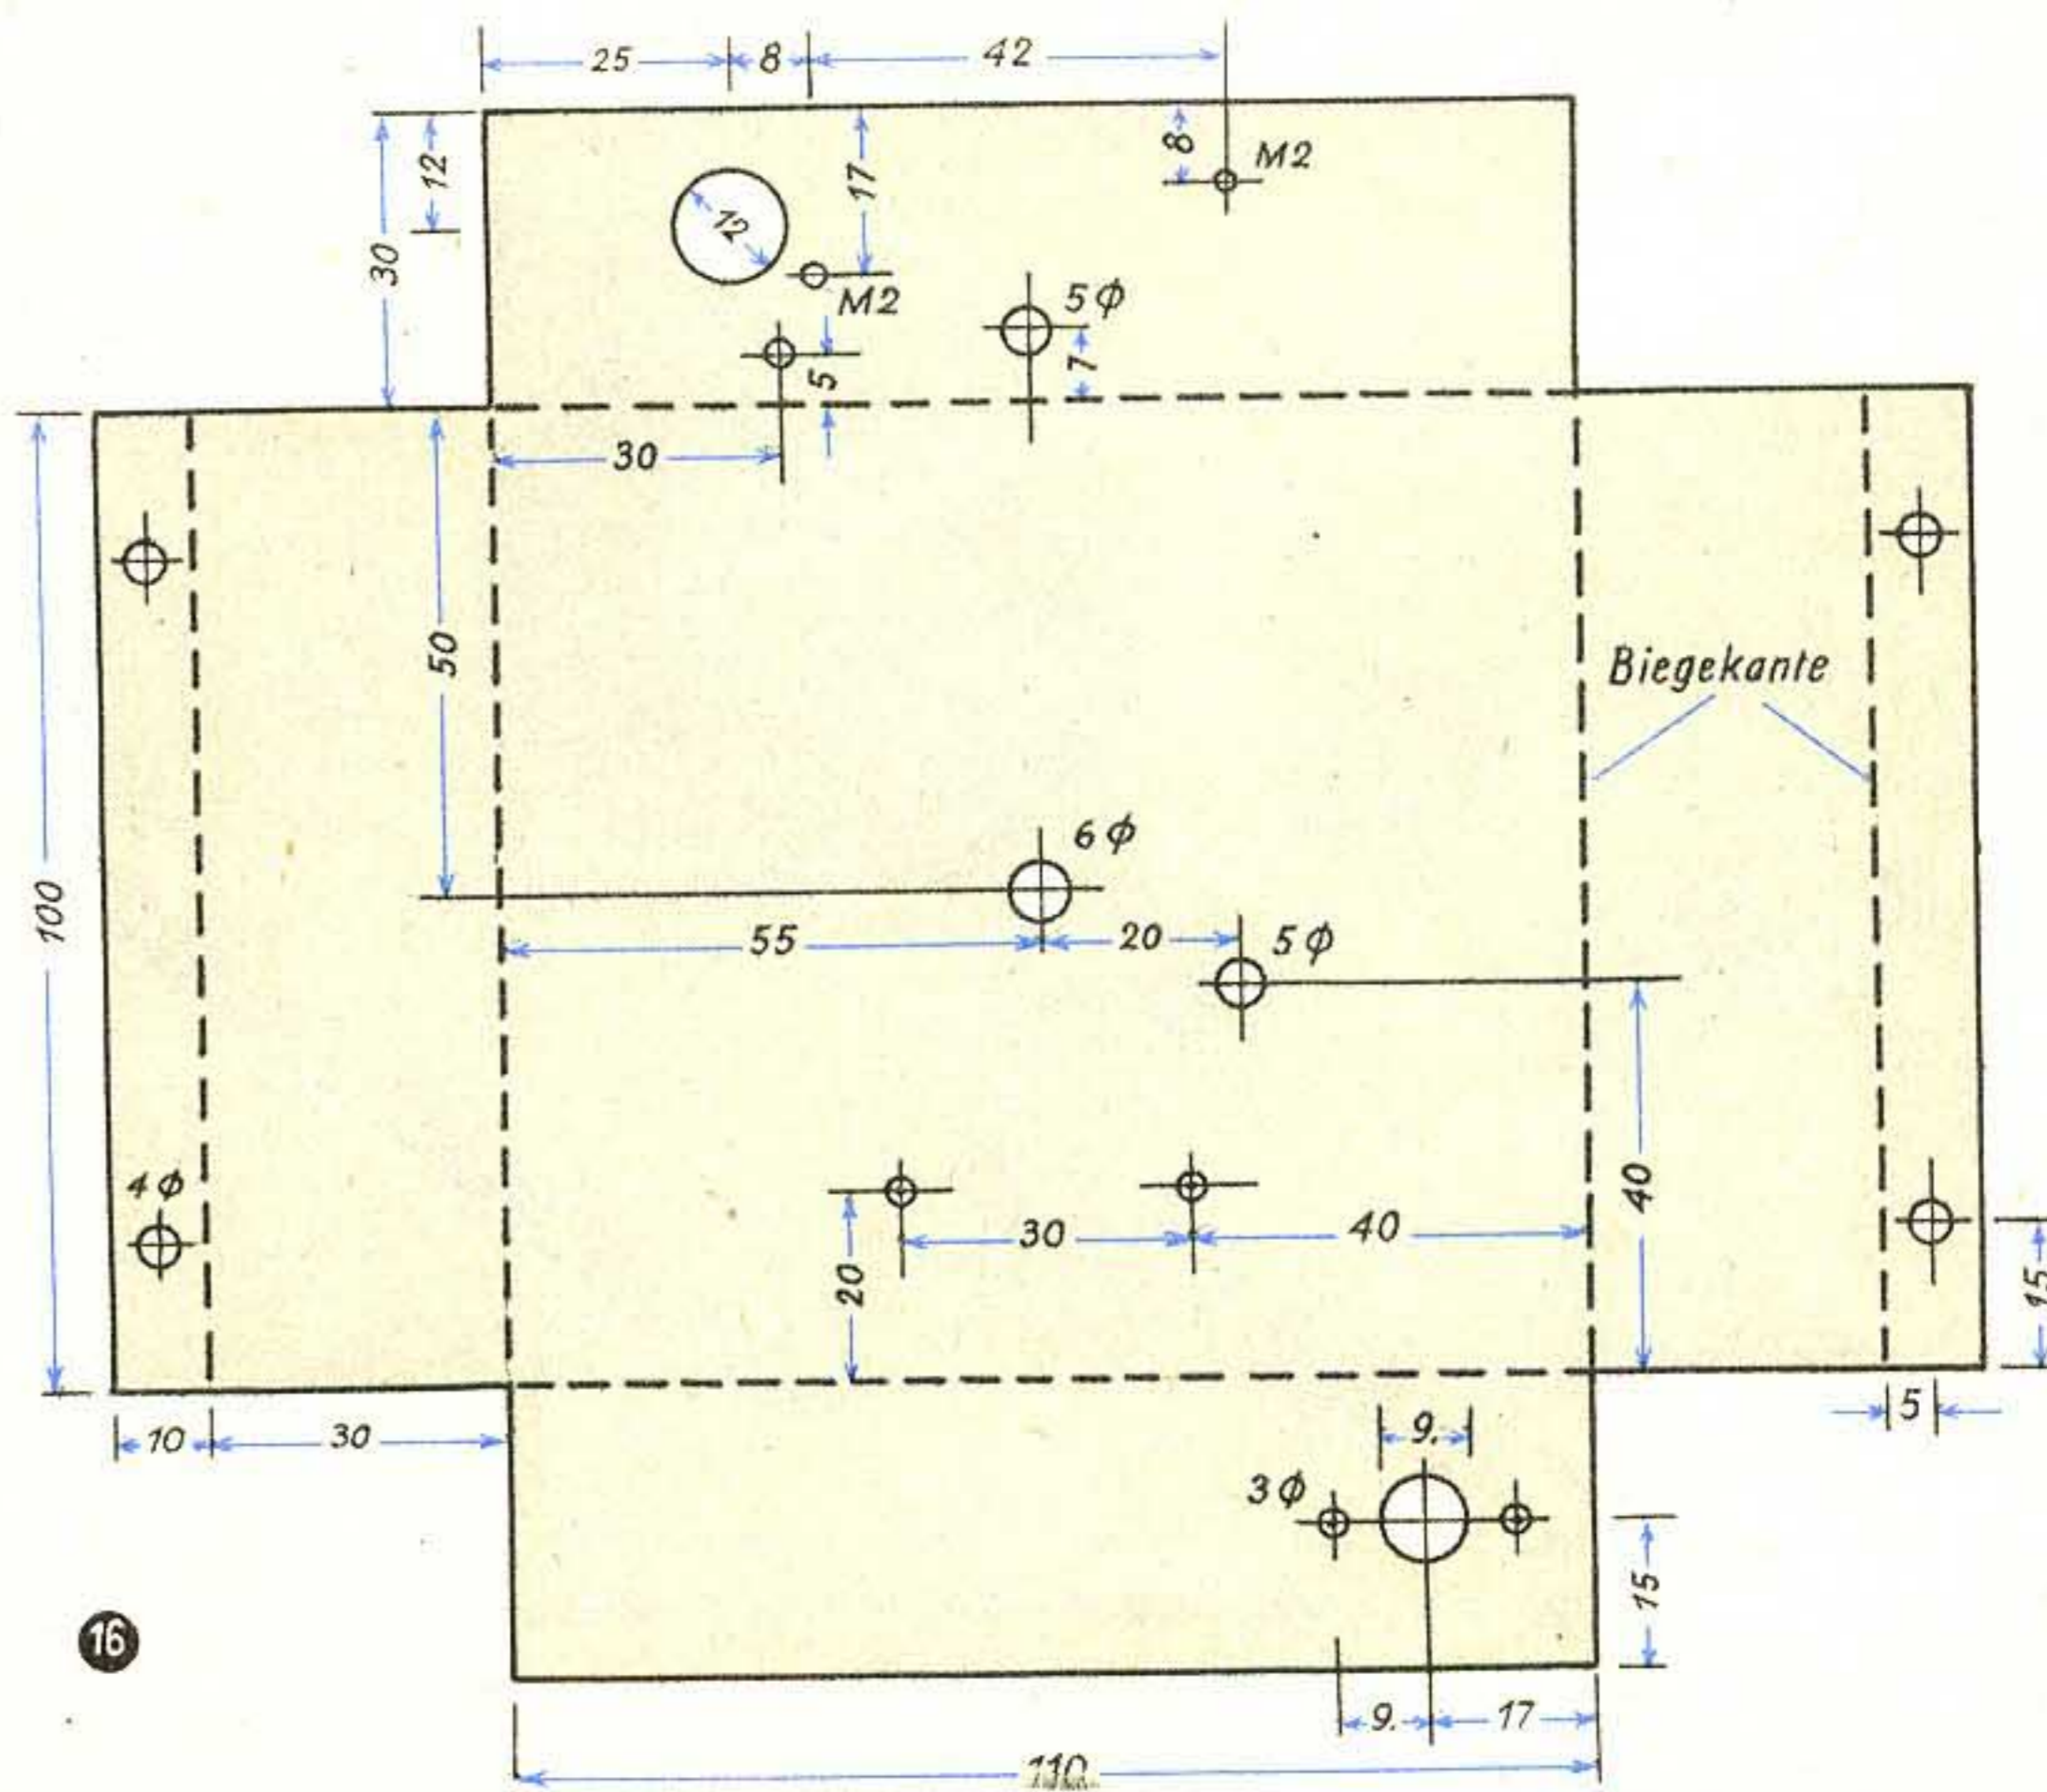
Maßskizze für das Verstärkerchassis; Material = 1-mm-Eisenblech
